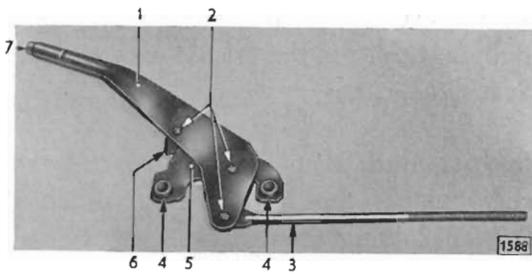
Zusammenbau Handbremshebel mit Zugstange
